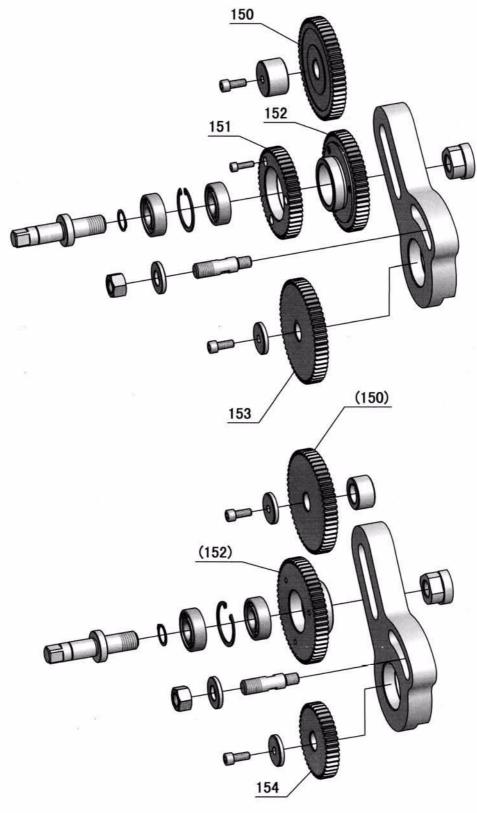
Wechselradgetriebe (Inch) - Change whell gear (Inch)
